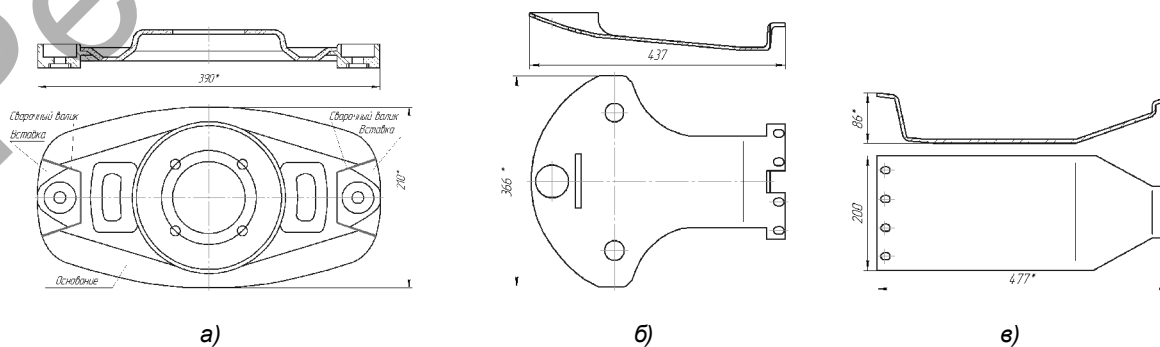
Эскизы диска ротора (а), основного (б) и дополнительного основания (в) башмаков бруса режущего аппарата косилок
